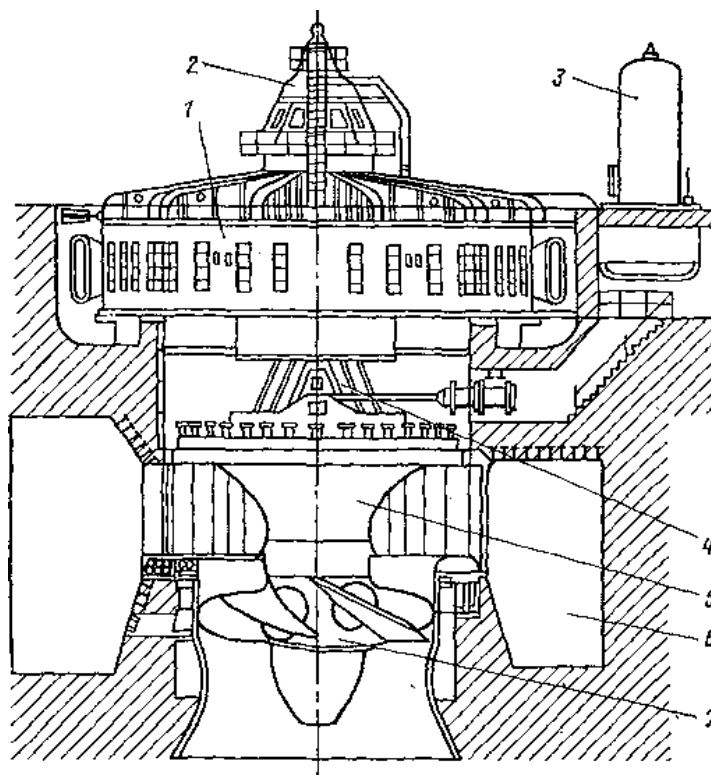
Компонівка агрегата с вертикальним валом:
